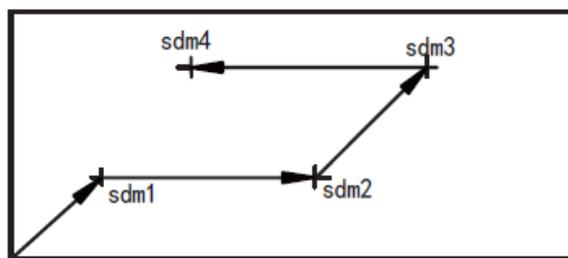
Нулевая точка заготовки (0.000) в ABS координатах.
